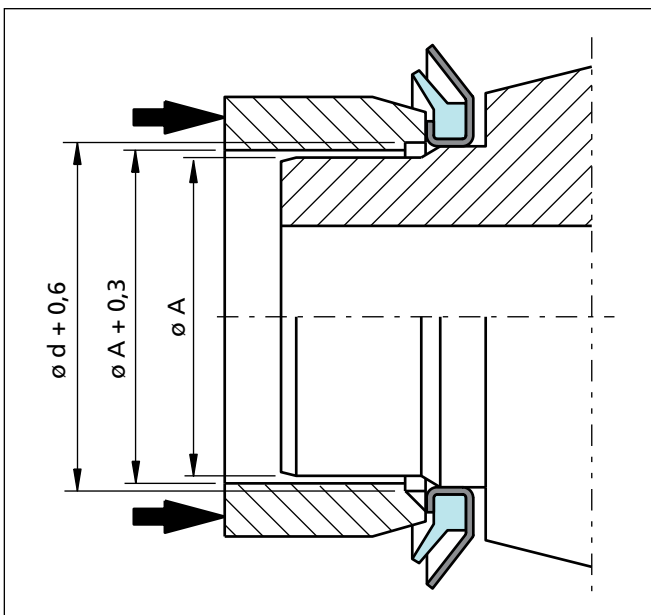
Montagewerkzeug. Bei der Montage gegen einen Ansatz darf die Montagekraft nicht zu groß sein, damit das Gehäuse des GAMMA-Ringes nicht beschädigt wird.
